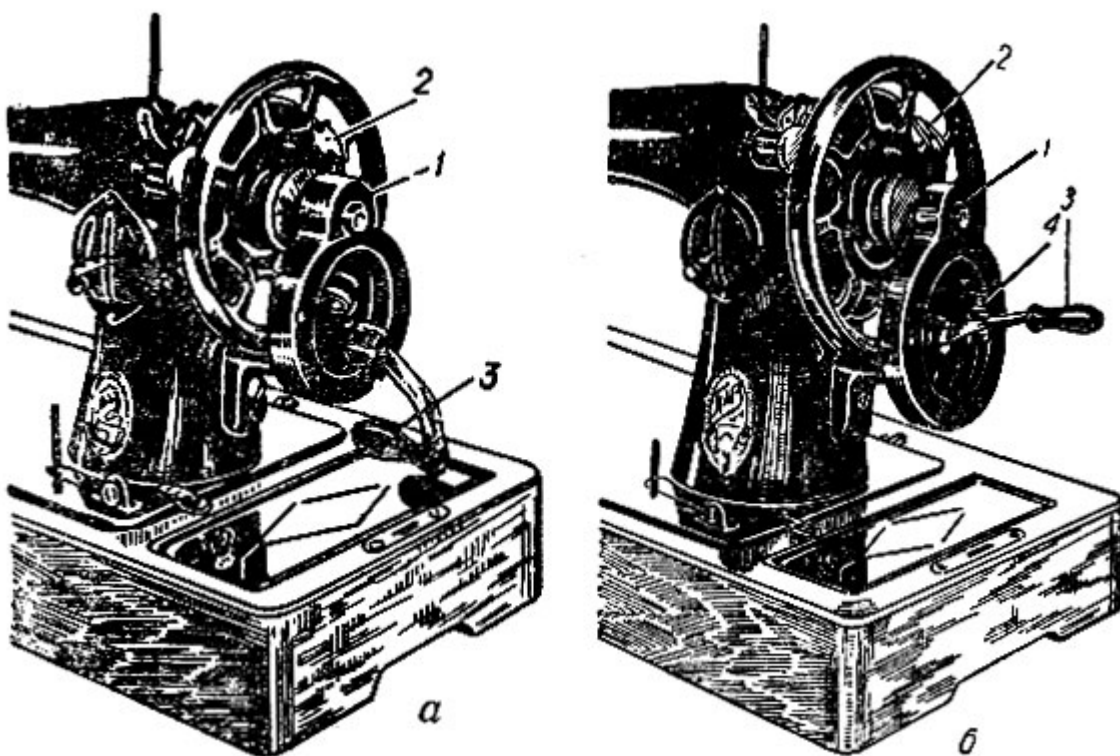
Ручной привод швейной машины 1-А класса ПМЗ: а - в нерабочем положении; б - в рабочем положении
